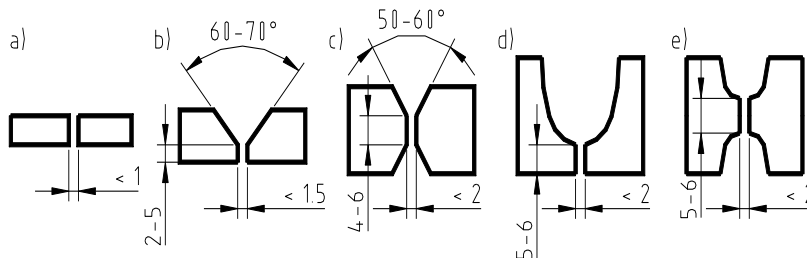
Tipos de preparação das peças para soldadura.
